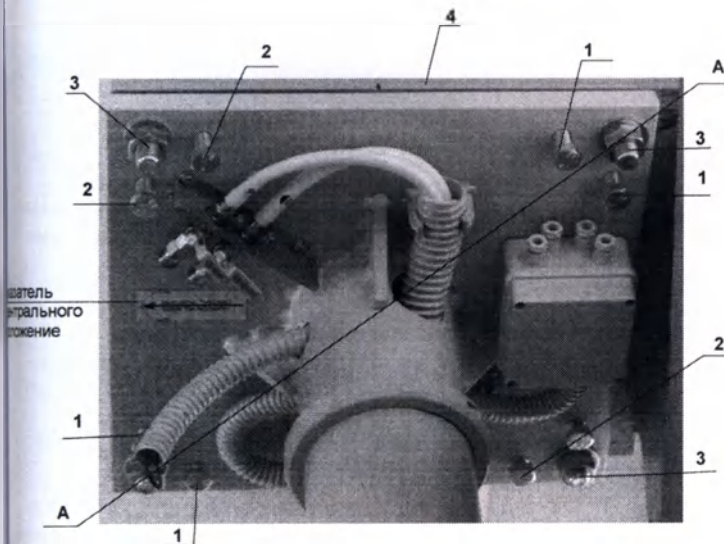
Расположение наклейки "центральное положение", регулировочных болтов и гаек крепления основания консоли (типовой вид)
